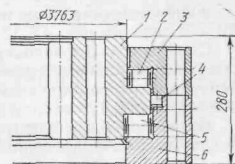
Поворотный сталеразливочный стенд конструкции «Демаг»
